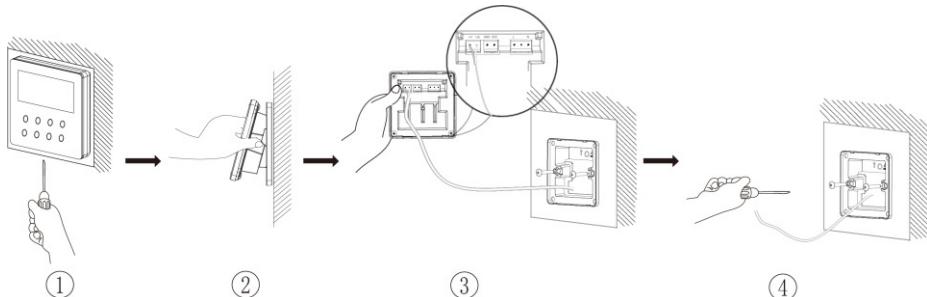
Diagrama de desmontaje del controlador por cable
